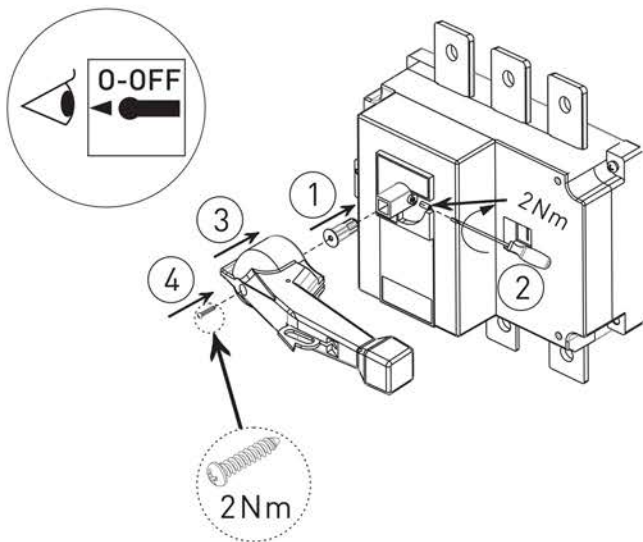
а – Монтаж ручки на корпус рубильников 160-630 А
